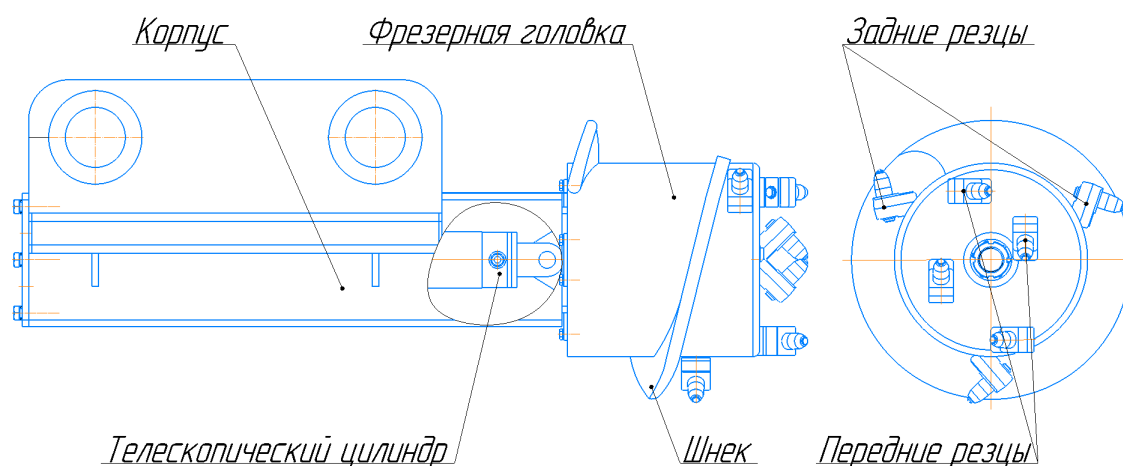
Общий вид фрезерного рабочего оборудования
